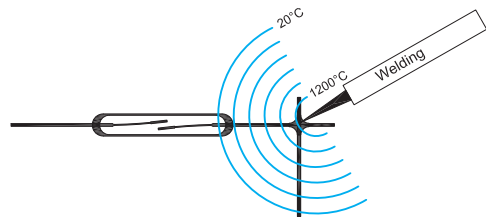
Löten und Schweißen kann einen Hitzeschock auf die Glas-Metalleinschmelzung erzeugen.
